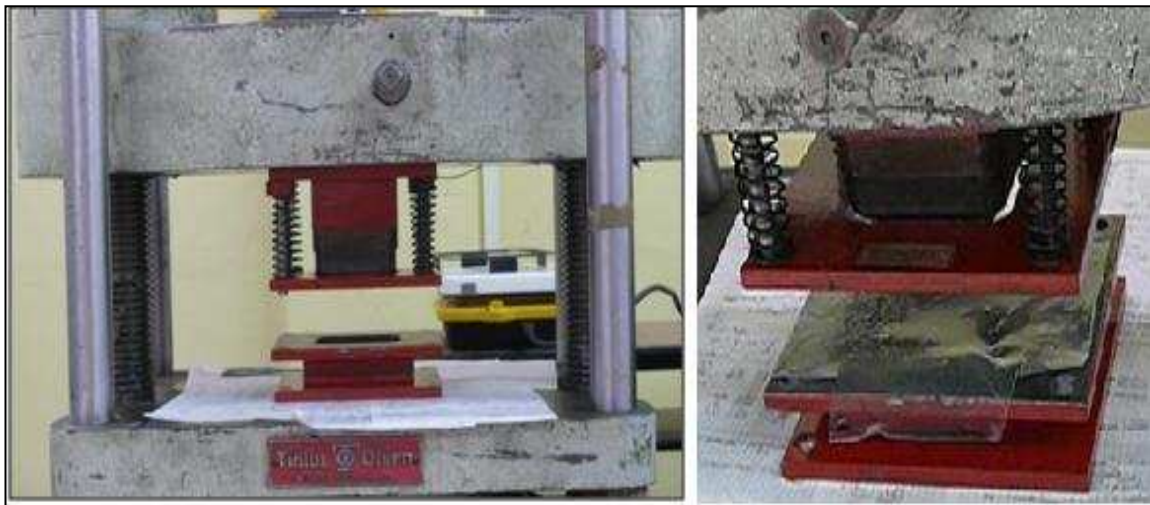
Termoformado de las láminas con el molde de acero ensamblado en la máquina universal de ensayos.
